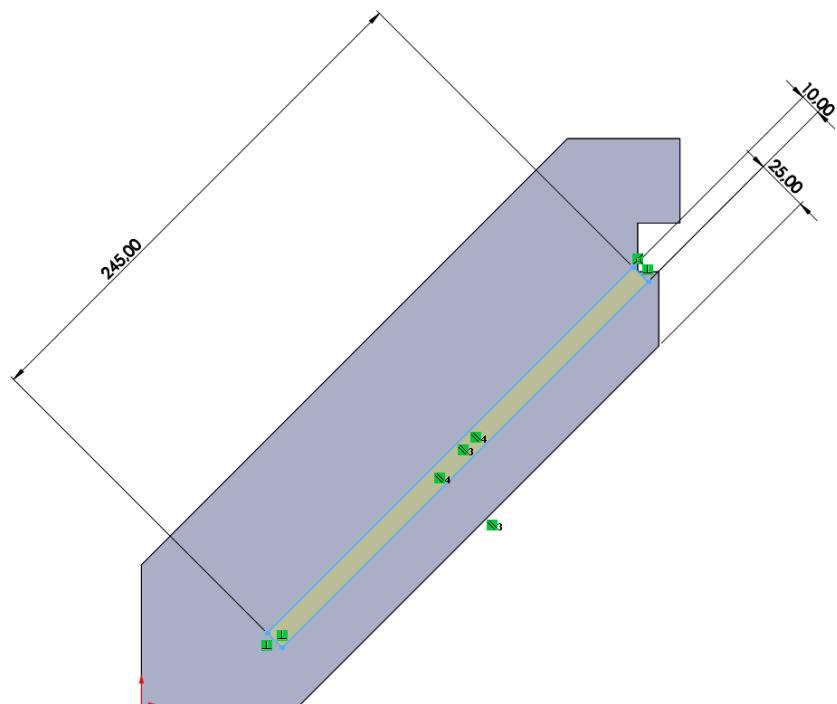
Эскиз детали «Рёбро в пластине»
